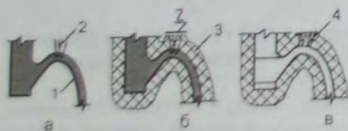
Схема выполнения ниточного выпора: 1 – стенка модели отливки; 2 – капроновая нить; 3 – КО; 4 – ниточный выпор
